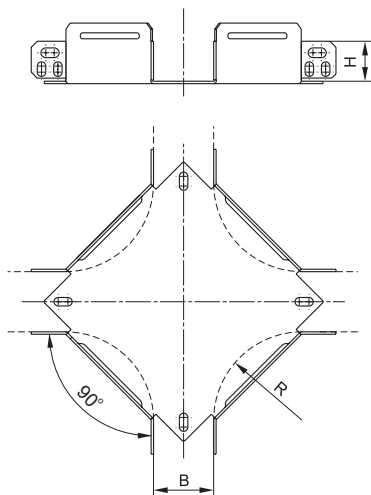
Крестовина. Размеры для размещения кабеля / Figure C.1 – Crossover. Dimensions for cable placement
